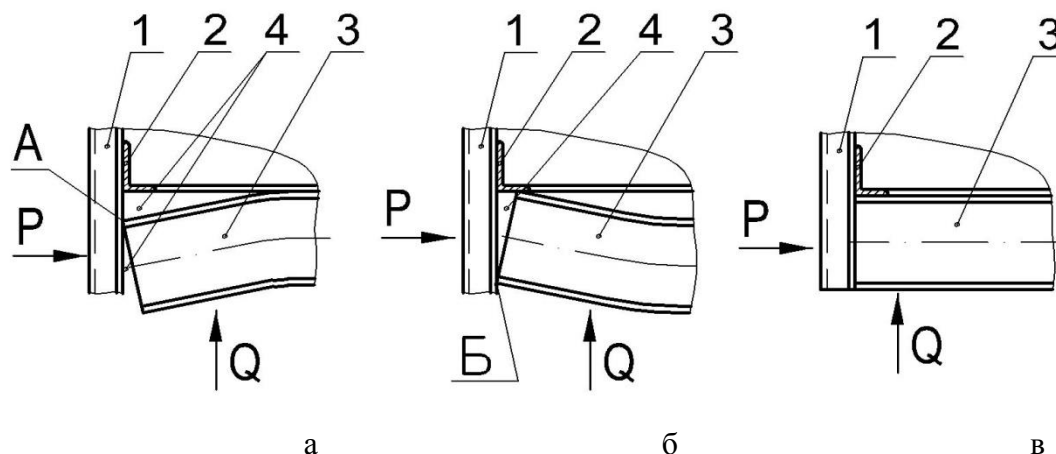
Схема образования зазоров в сварных стыках между балками рамы и уголками и стойками каркасов боковых стен при сборке кузова полувагона: а – при упоре верхней кромки балки (грань А) в стойку каркаса боковой стены; б - при упоре нижней кромки балки (грань Б) в стойку каркаса боковой стены; в – сборка стыков без зазоров:
